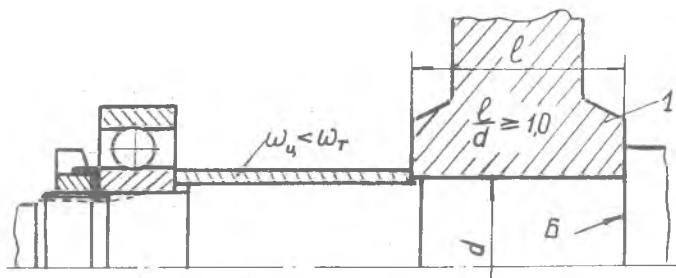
Крепление в упор к торцу вала колеса с длинной ступицей, втулки и подшипника
